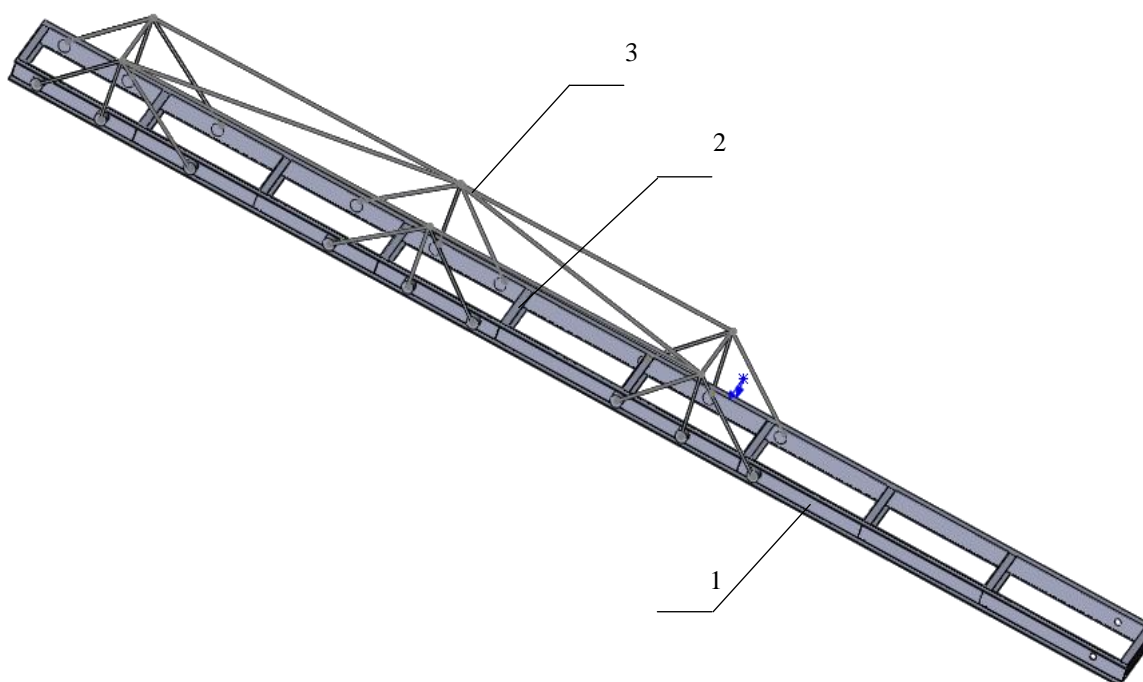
Предлагаемая конструкция рамы поворотного конвейера:
